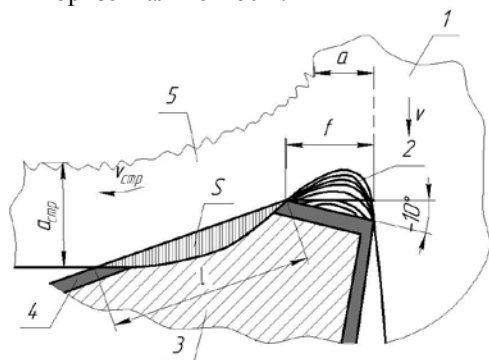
Схема испытаний покрытий на износостойкость при резании 1 – обрабатываемый материал; 2 – застойная зона; 3 – резцовая пластина из быстрорежущей стали; 4 – покрытие; 5 – стружка, S – площадь очага износа
